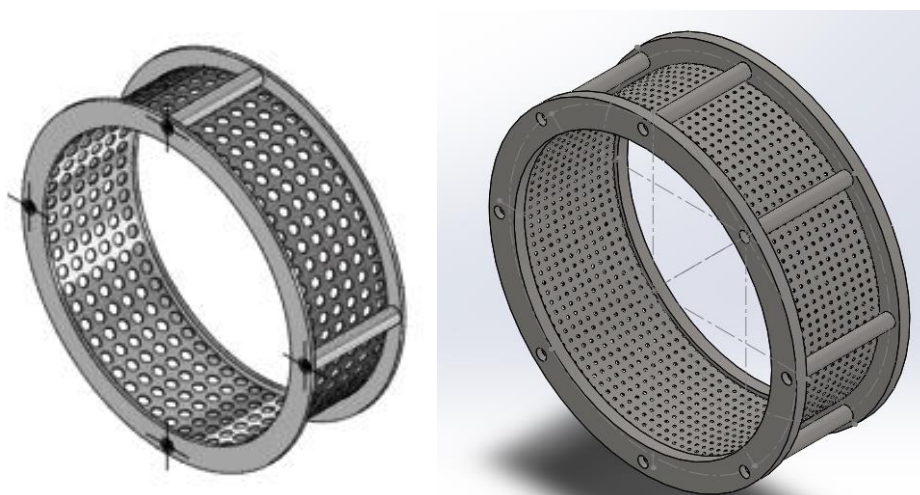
Vista 3D del conjunto tamiz circular. Izq: diseño anterior [1], Der: diseño actual.
